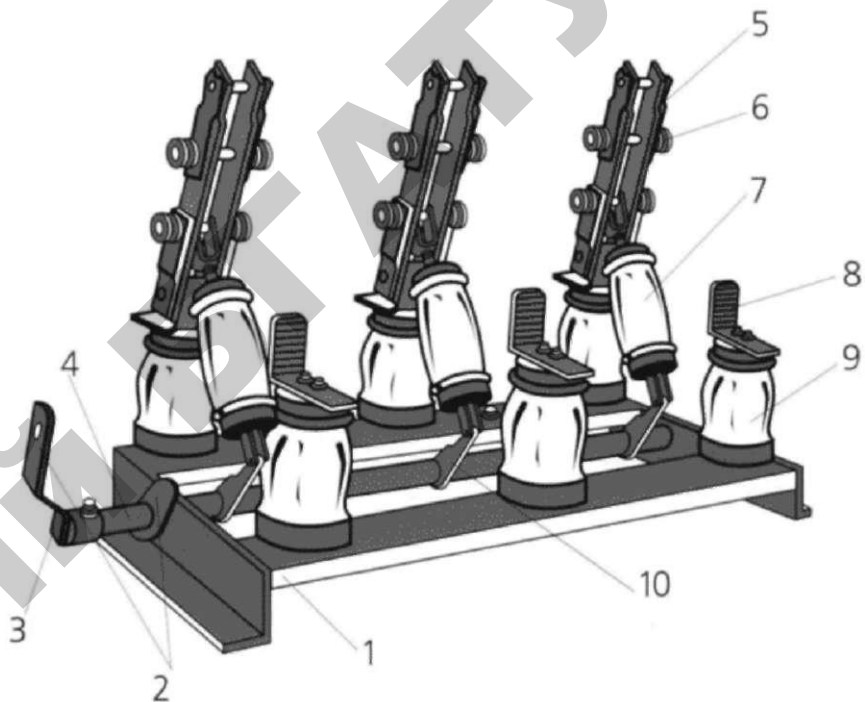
Разъединитель внутренней установки типа РВ-10:
